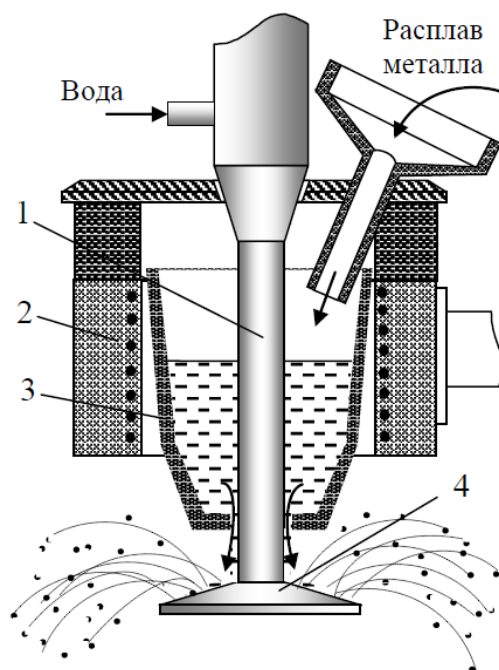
Схемы ультразвукового диспергирования расплавов металлов: 1 – концентратор колебаний; 2 –нагревательное устройство; 3 – контейнер с расплавом; 4 – излучатель
